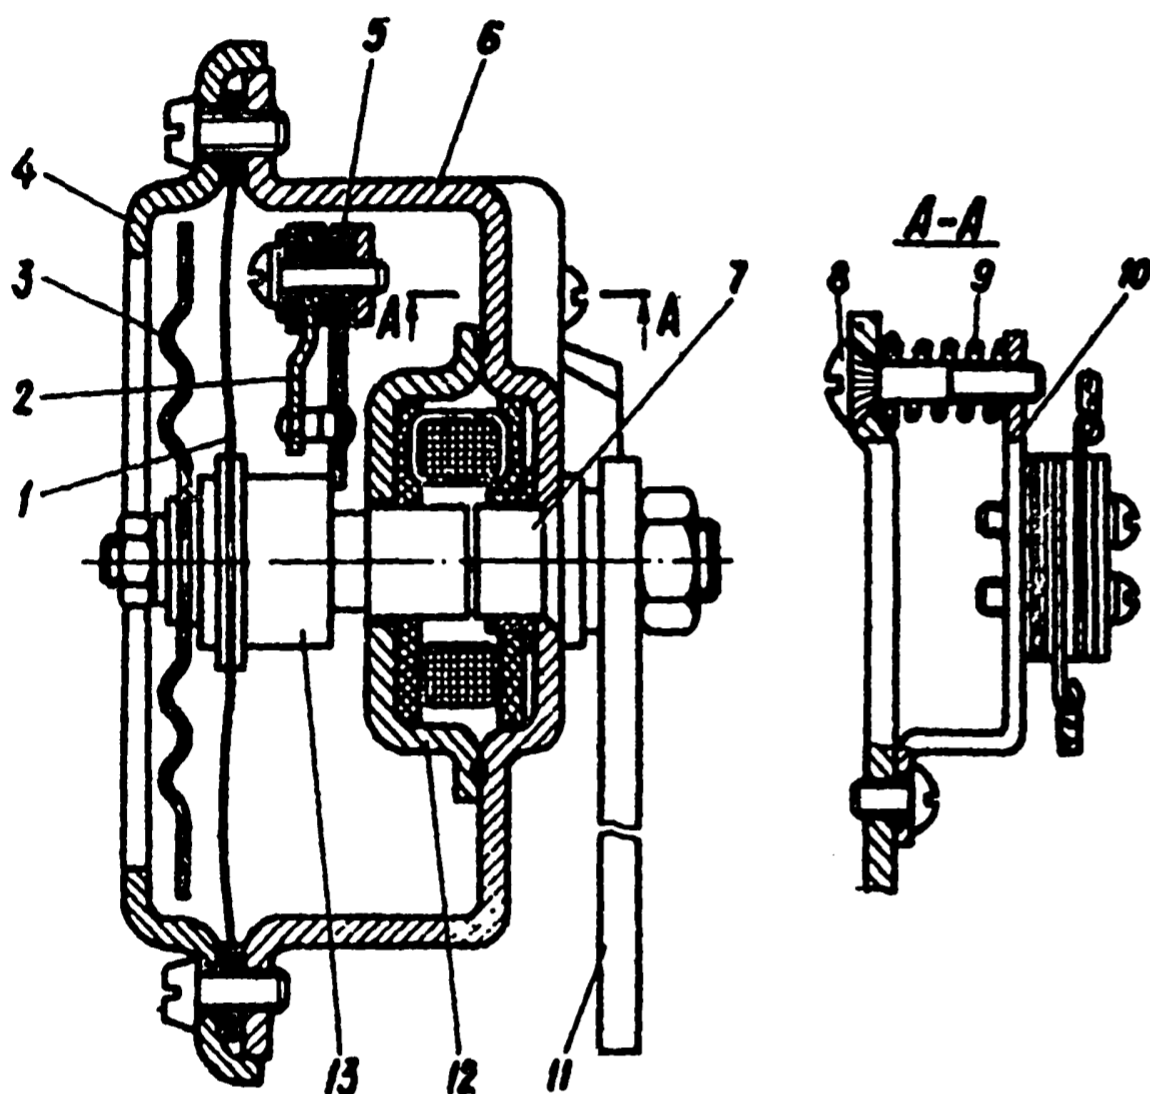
Звуковой сигнал С-304: 1 - мембрана; 2 - держатель неподвижного контакта; 3 - диффузор; 4 - кольцо; 5 - пластина подвижного контакта; 6 - корпус; 7 - сердечник; 8 - регулировочный винт; 9 - пружина регулировочного винта; 10 - мостик; 11 - пластина крепления сигнала; 12 - ярмо; 13 - якорь
